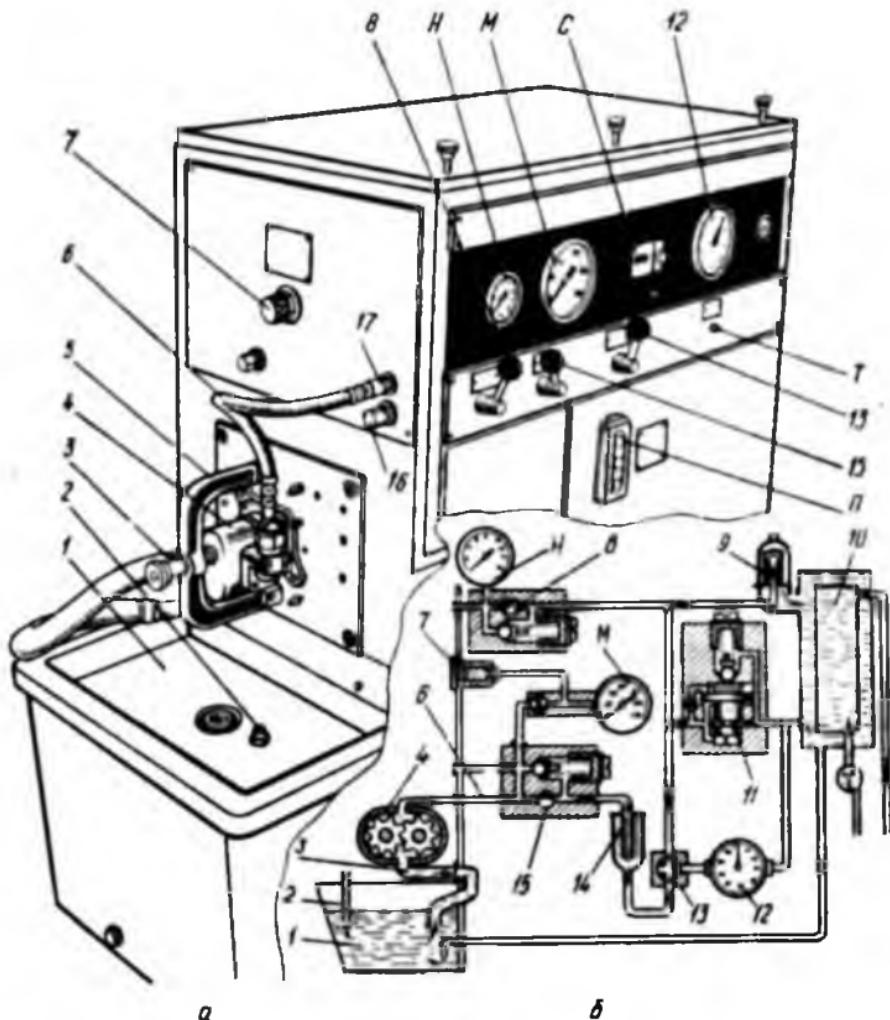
Установки насоса (а) и схема присоединения его к гидросистеме (б) стенда КИ-4200:
